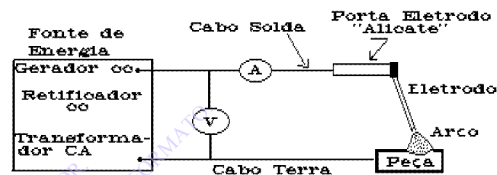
Sistema essencial para a soldagem com eletrodo revestido.
